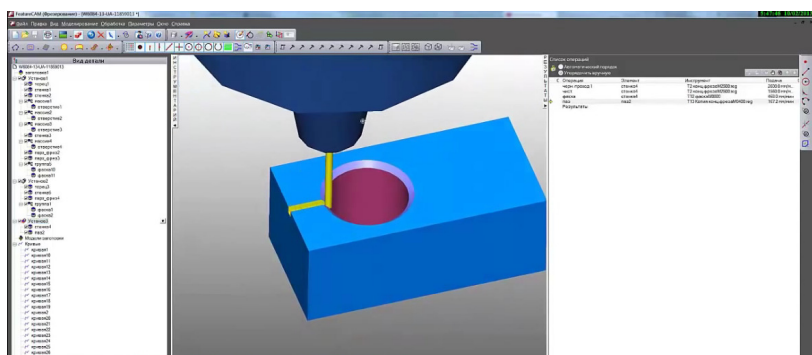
Модуль FeatureMILL для фрезерної обробки.
